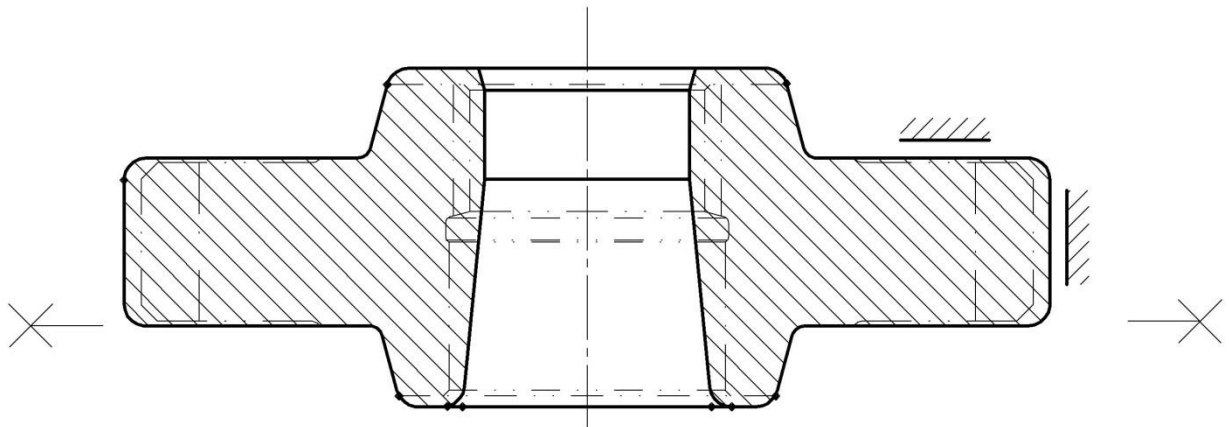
Общий вид заготовки детали - «Шестерня»
